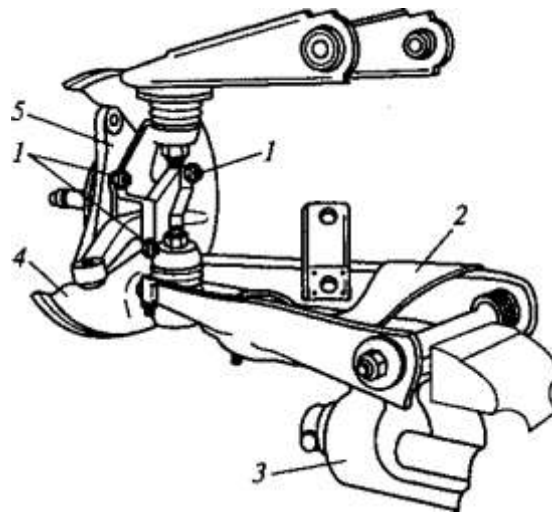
Вузол підвіски лівого колеса, закріплений на верстаті для розбирання:
